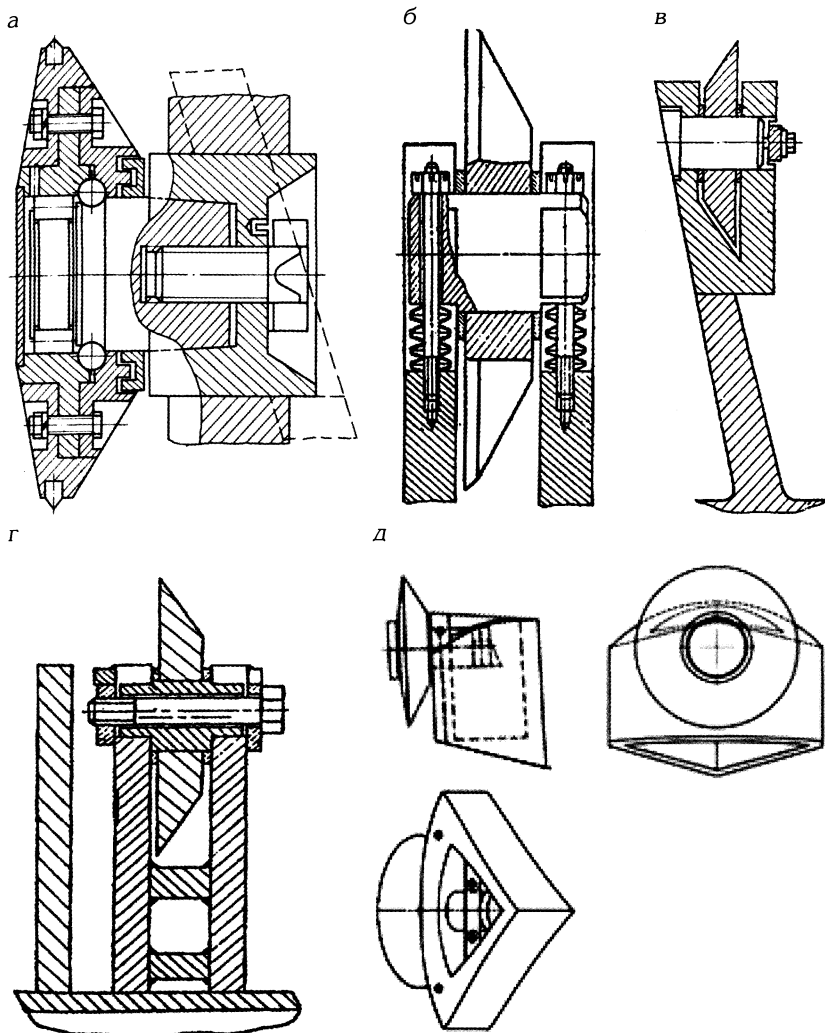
Конструктивные особенности узлов крепления дисковых инструментов: а — патент РФ № 2239059; б — а.с. № 1456558; в — а.с. № 1555481; г — а.с. № 1280119; д — патент РФ № 2455486
